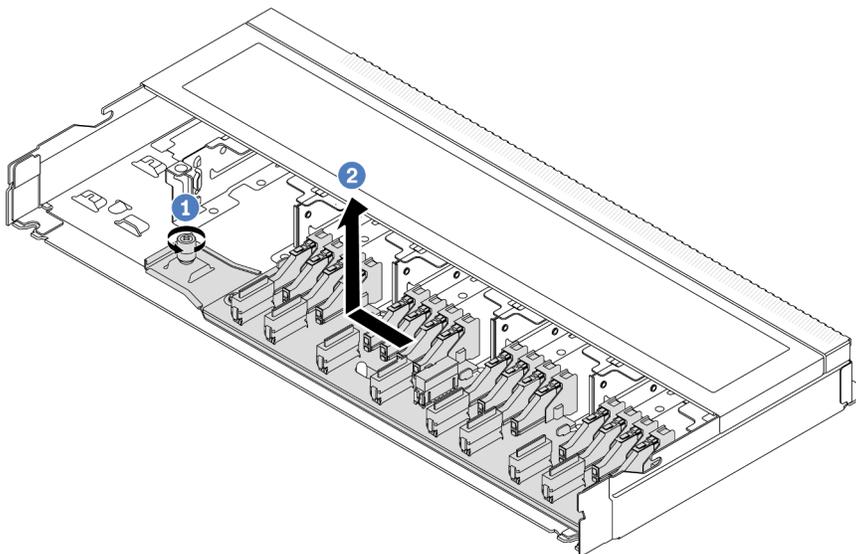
Entfernen einer Rückwandplatine für 16 EDSFF-Laufwerke
